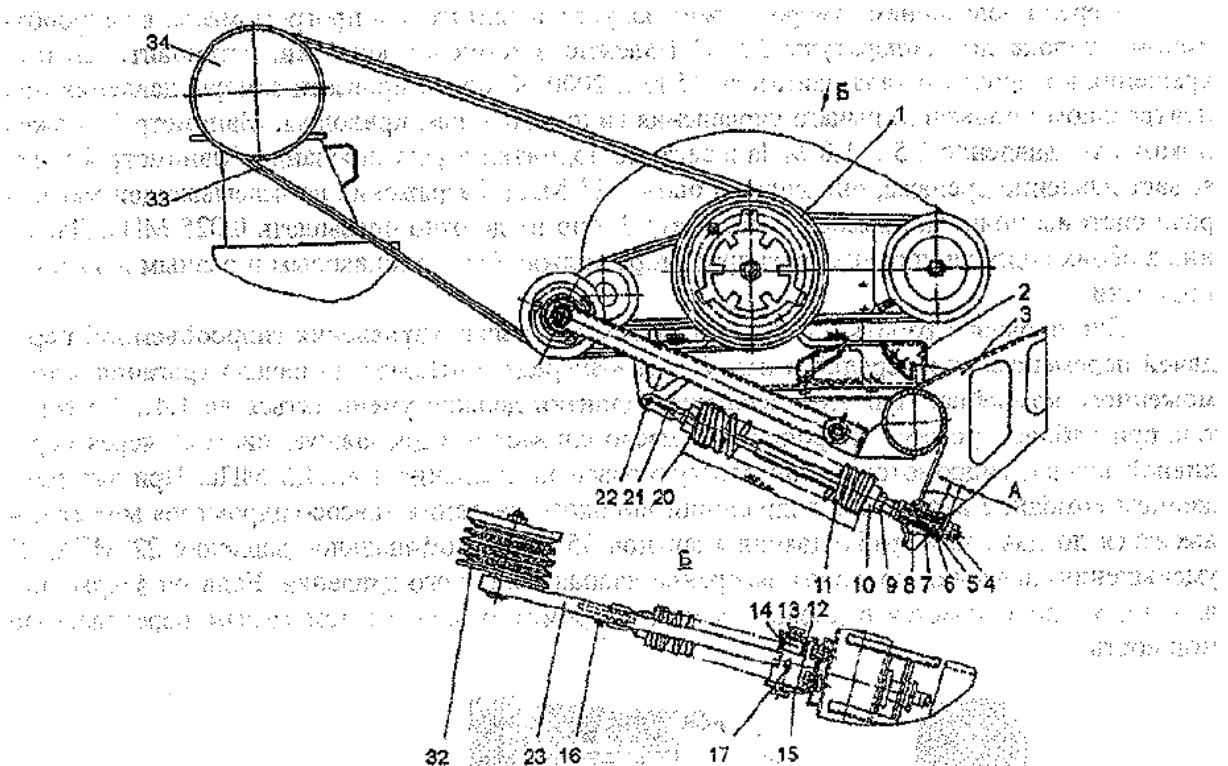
Привод гидронасоса ходовой части комбайна «Дон-1500Б»: 1-шкив двигателя; 2-рама моторно-силовой установки; 3-кронштейн рамы; 4, 9-гайки; 5-шайба; 6- амортизатор; 7-шпилька; 8-втулка натяжная; 10, 20-пробки; 11-пружина; 12, 14-шайбы; 13-втулки; 15- кольцо стопорное; 16-масленка; 17, 22-оси; 21- вилка; 23-рычаг шкива; 32-шкив натяжной; 33-ремень приводной; 34-шкив привода гидронасоса; А-толщина амортизатора 6, равная 13...15 мм
